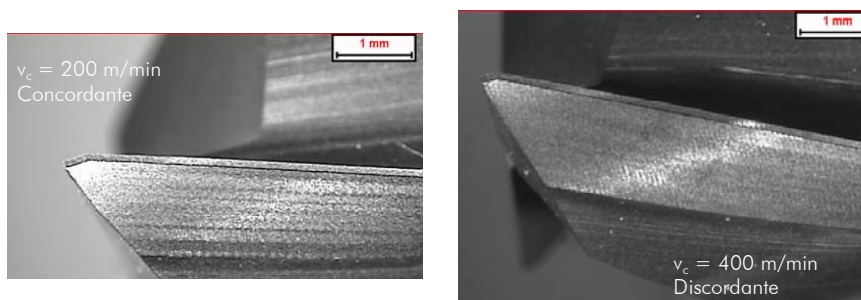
Desgaste de flanco uniforme para VB = 0,1 mm.
